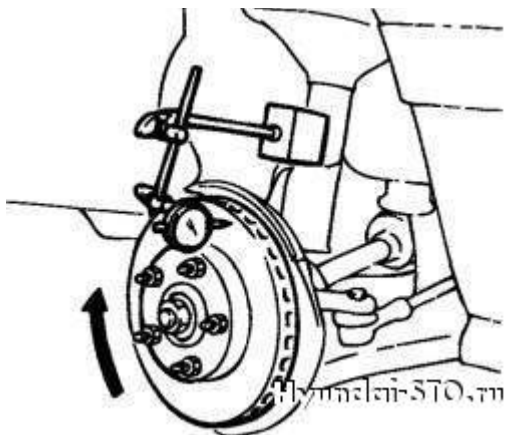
(#) Měření axiální vůle v ložisku náboje
